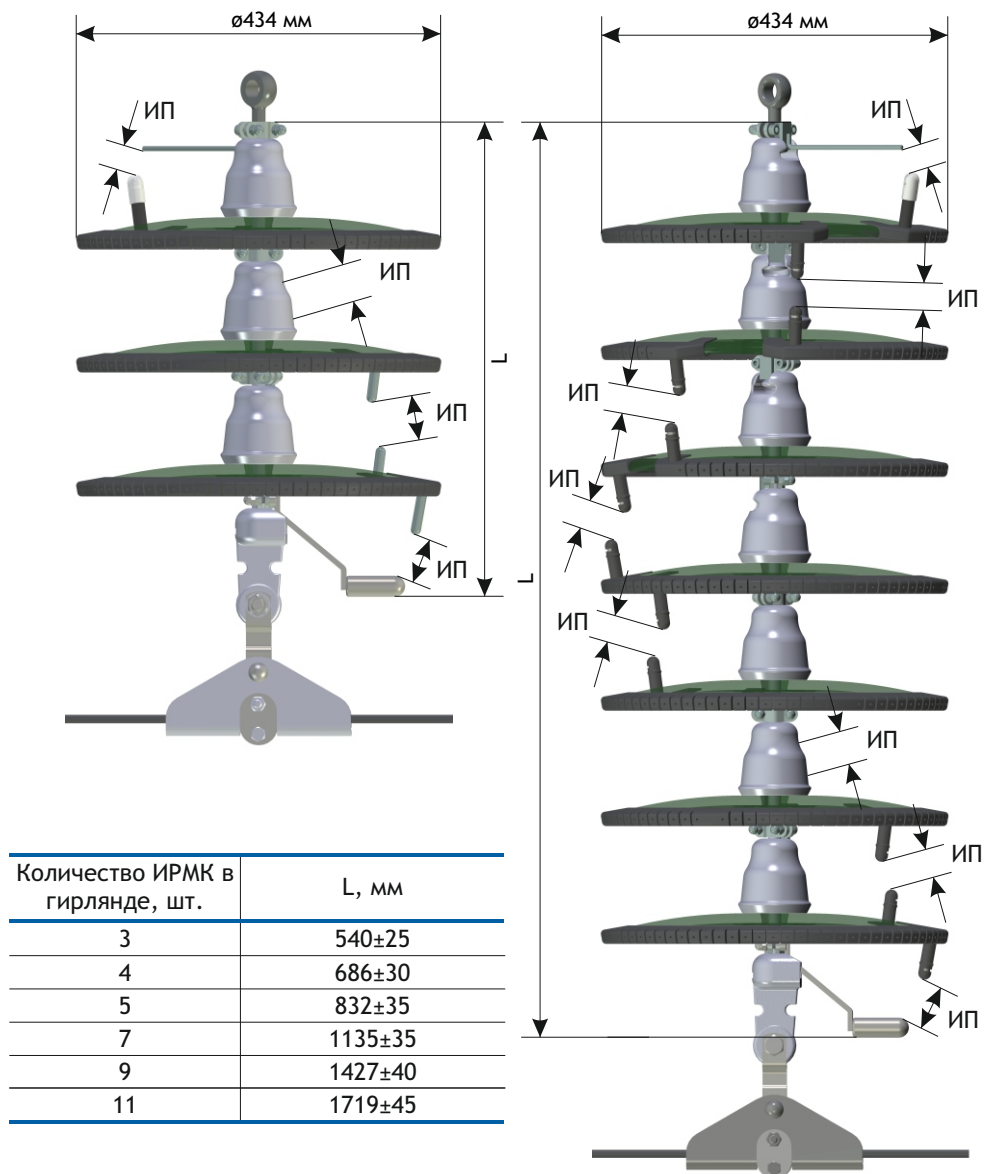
Эскиз установки, а также габаритные, установочные и присоединительные размеры
